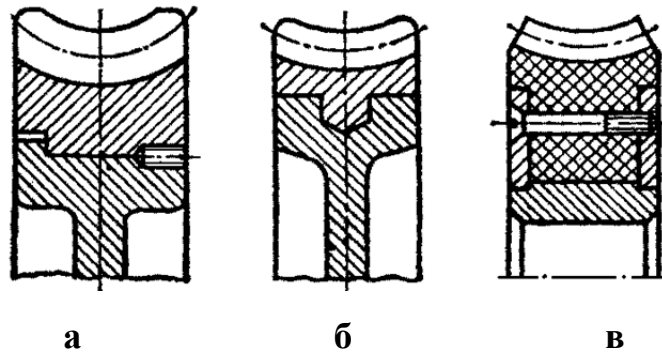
Типи з'єднання вінця черв'ячного колеса з маточиною:
